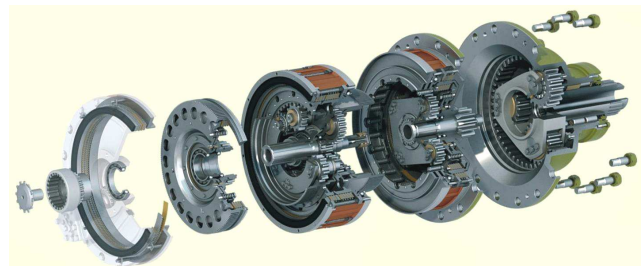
3D-модель бортової коробки передач згідно [6]
